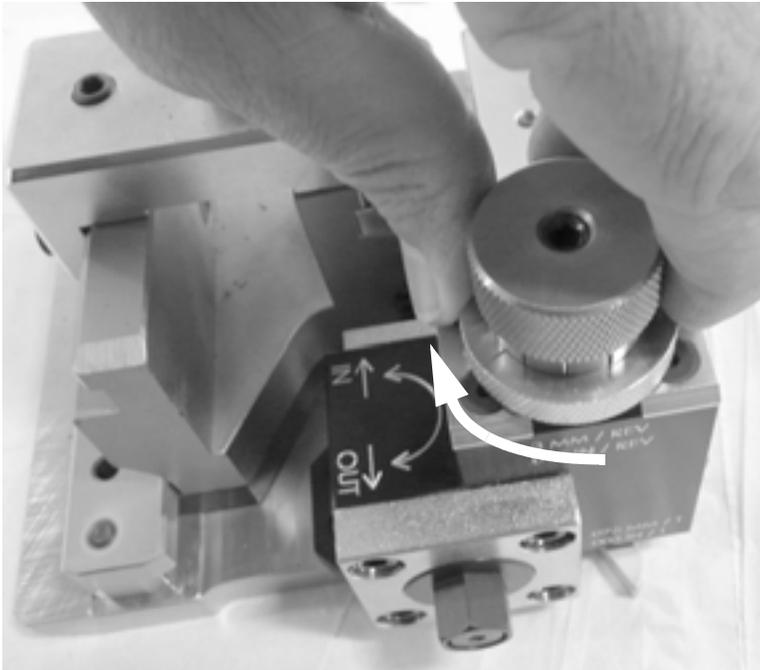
Die Standard-Werkzeugschlitten sind mit ihren Betriebsmaßen beschriftet.
